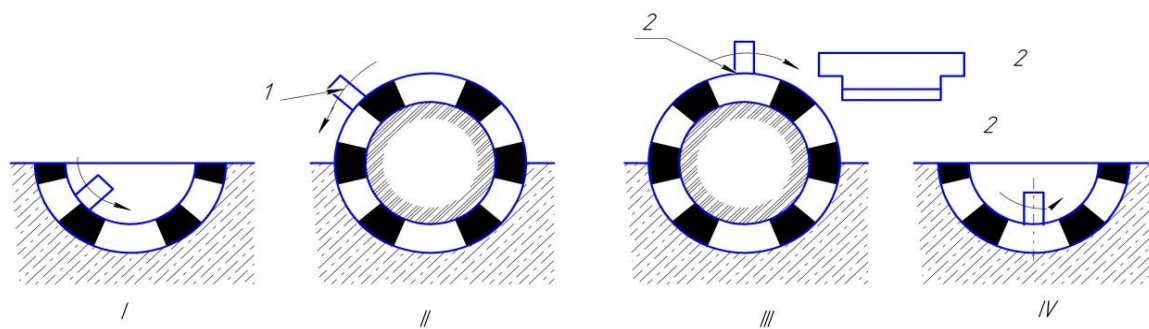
Схема формовки по скелетным моделям: *I* - отделка внутренней поверхности формы; *II* - формовка стержня; *III* - отделка стержня; *IV* - отделка внешней поверхности формы; 1, 2 – шаблоны
